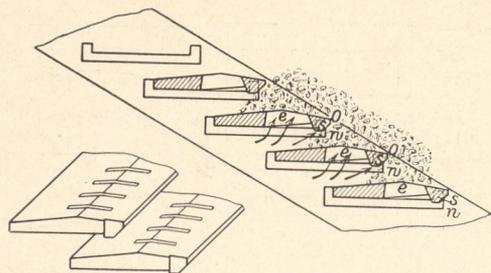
Rostplatten. Bauart: Strube-Lange. D. R. P.
